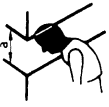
Schützende Konstruktion mit eingeschränkter Öffnung
